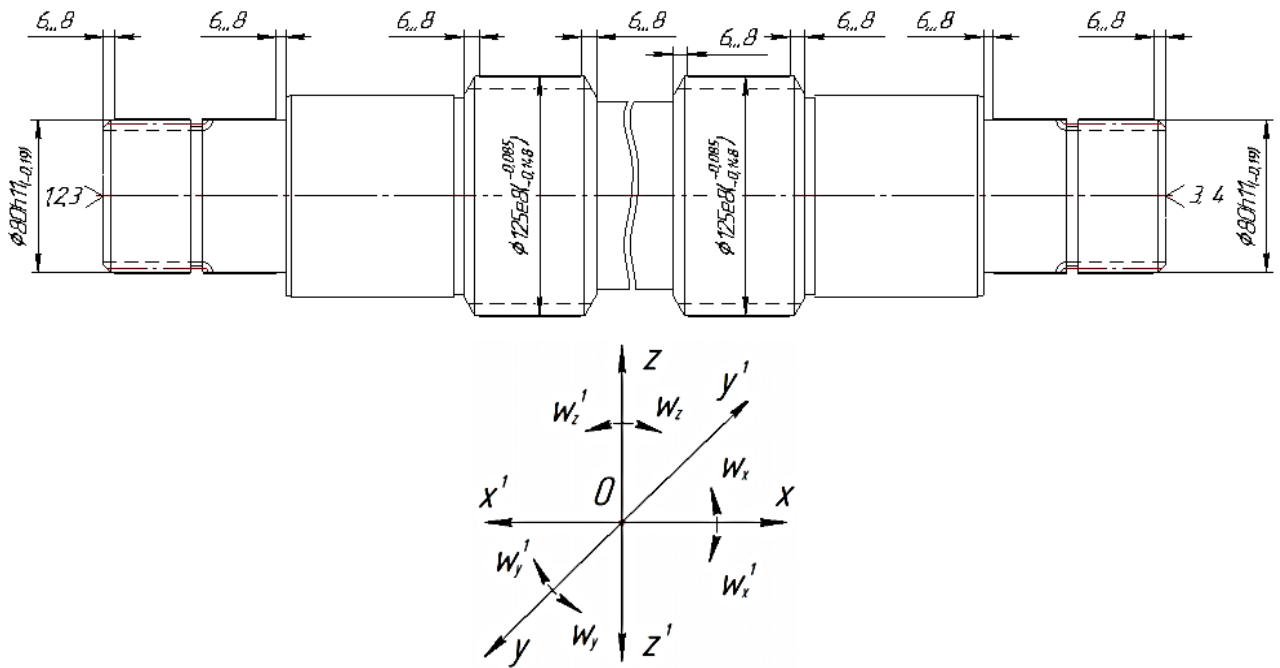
Схема базування деталі «Вал-шестерня»
